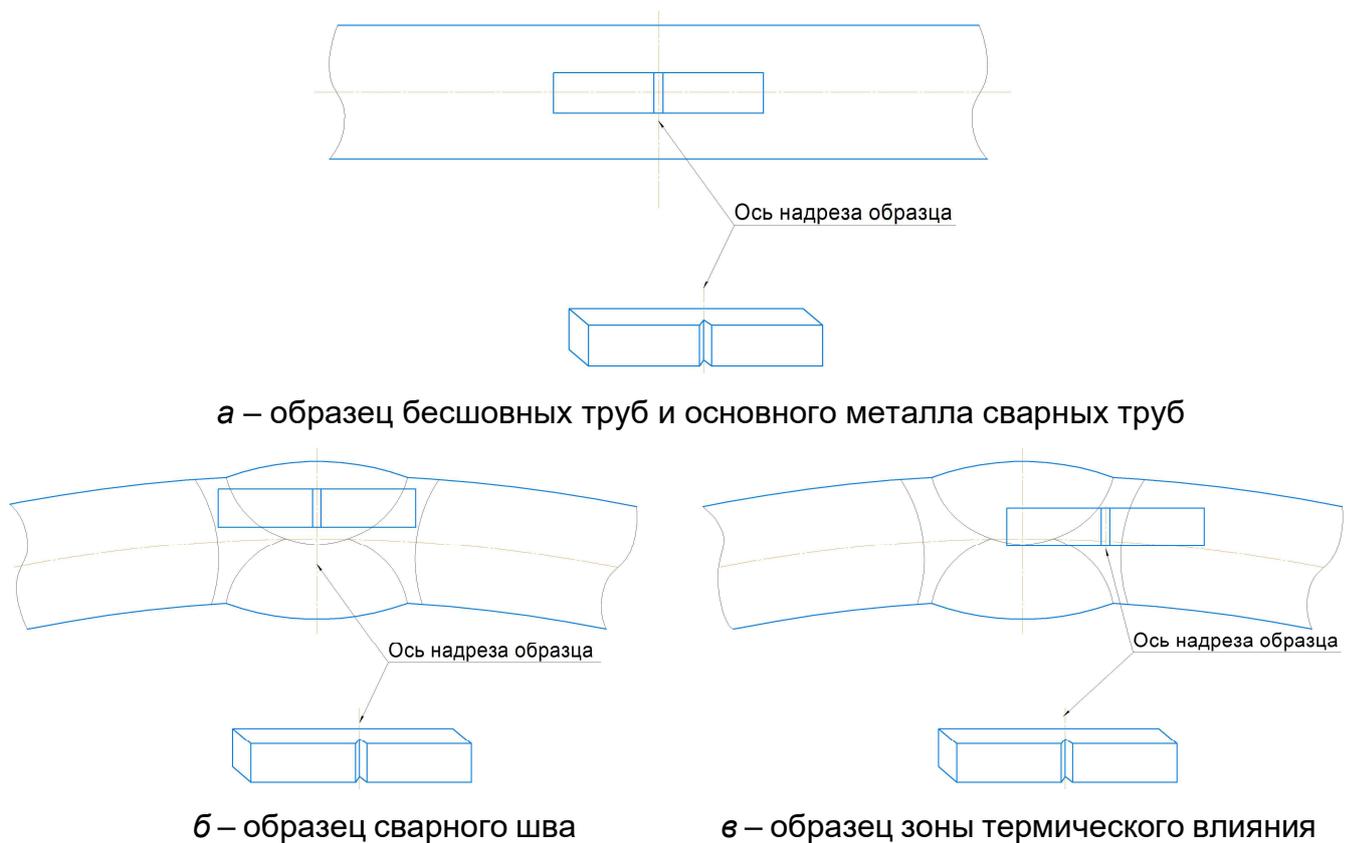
Расположение образцов для испытаний на ударный изгиб сварных труб
